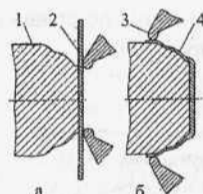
Схема ротационной раскатки диска: а – исходное положение; б – конечное положение; 1 – оправка; 2 – заготовка; 3 – ролики; 4 – диск
